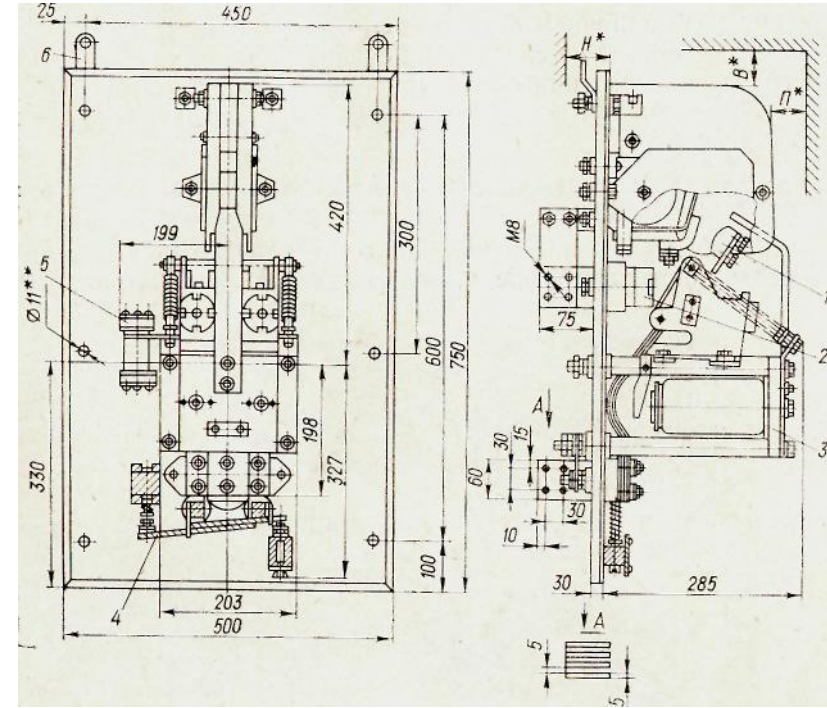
Габаритные, установочные, присоединительные размеры контакторов:
